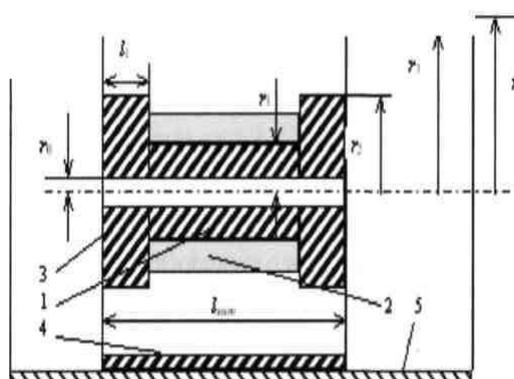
Схема конструкции индуктора магнитной установки УМП
